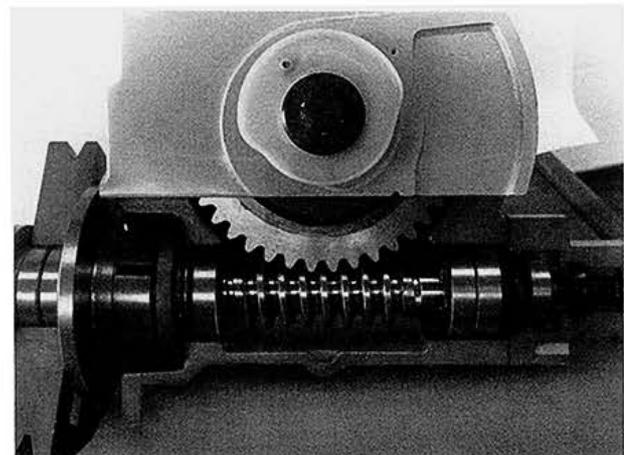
Schneckenradgetriebe des Messerantriebes einer Schneidemaschine mit hydraulisch bewegter Kupplung
